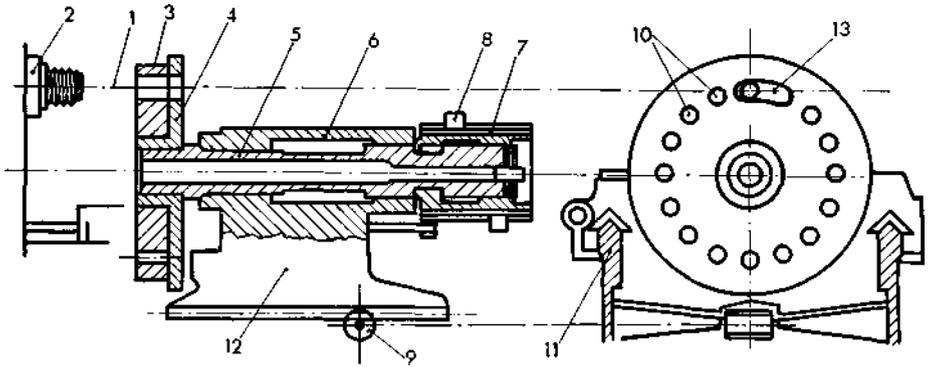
Revólver de tambor del torno americano PITTER. — 1, Eje de puntos teórico. — 2, Eje principal. — 3, Tambor del revólver. — 4, Plato del tambor. — 5, Eje del plato del tambor. — 6, Soporte del eje. — 7, Tambor de topes. — 8, Topes regulables — 9, Piñón de traslación del carro longitudinal. — 10, Taladros para montaje de las herramientas. — 11, Guías bancada. — 12, Carro revólver. — 13, Alojamiento alargado para el tronzado de piezas largas.
